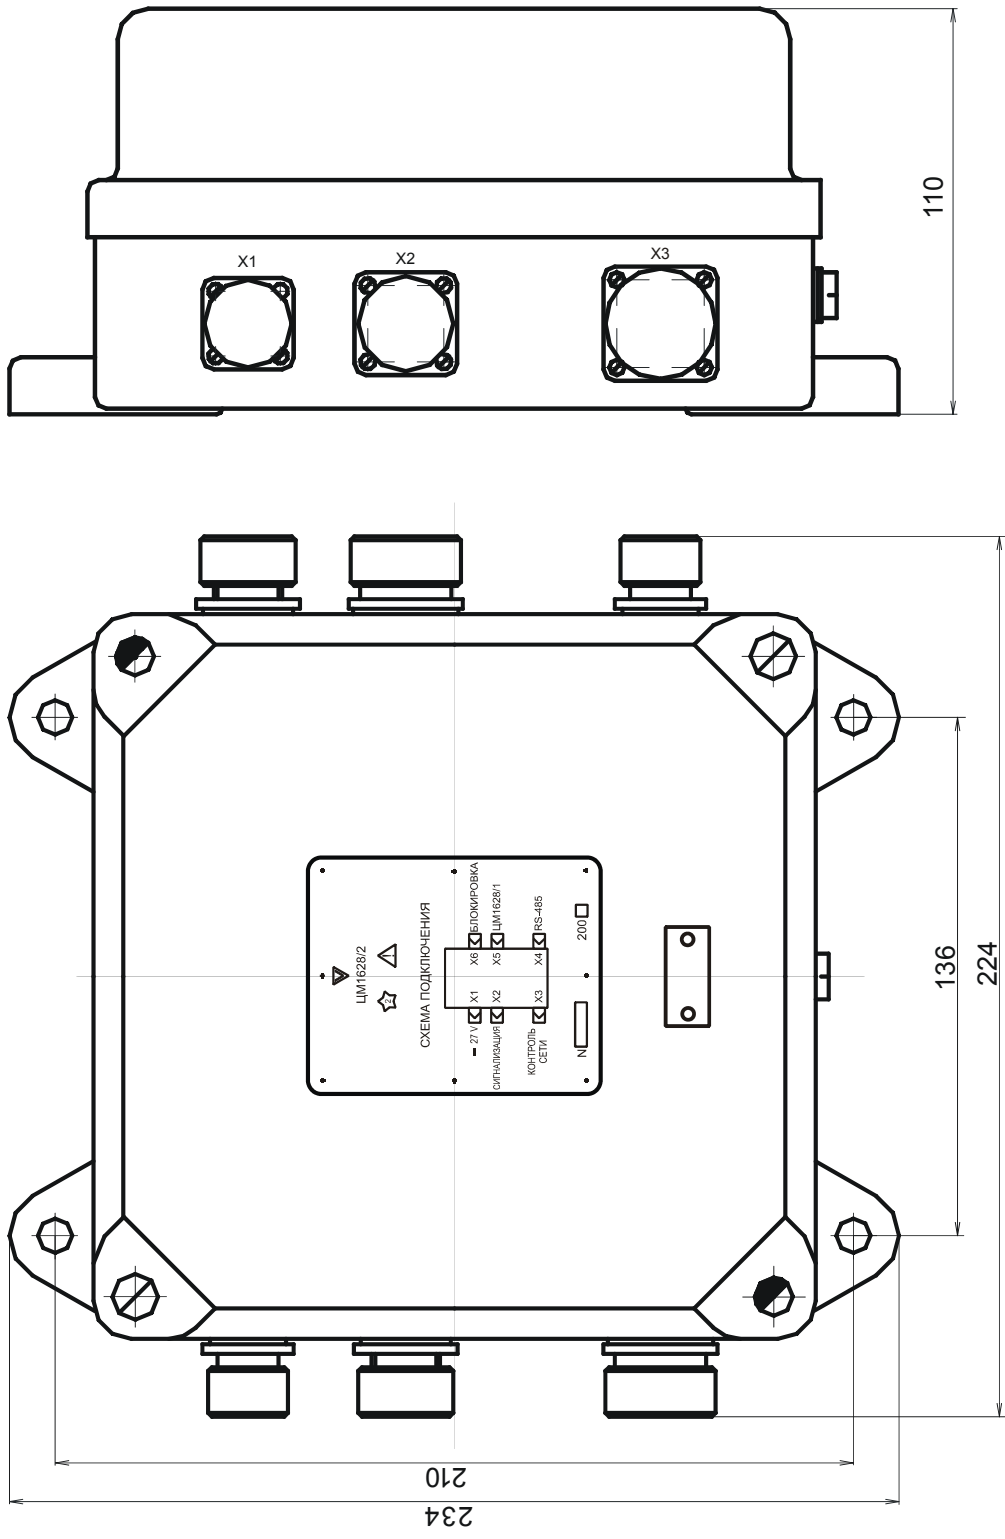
Внешний вид и габаритные размеры блока ЦМ1628/2
